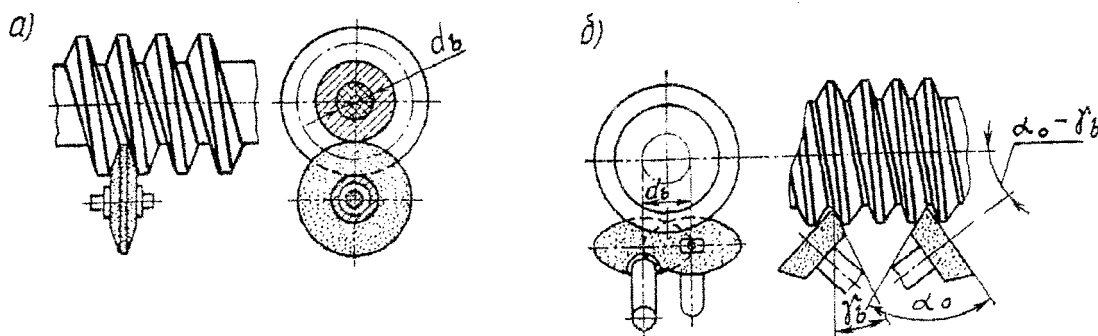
Схемы установки шлифовальных кругов при шлифовании эвольвентных червяков ZJ:
